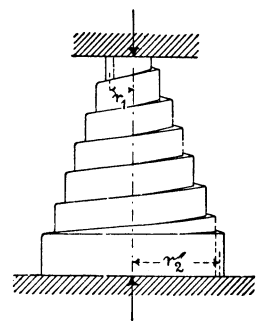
Kegelfeder mit rechteckigem Querschnitt.
